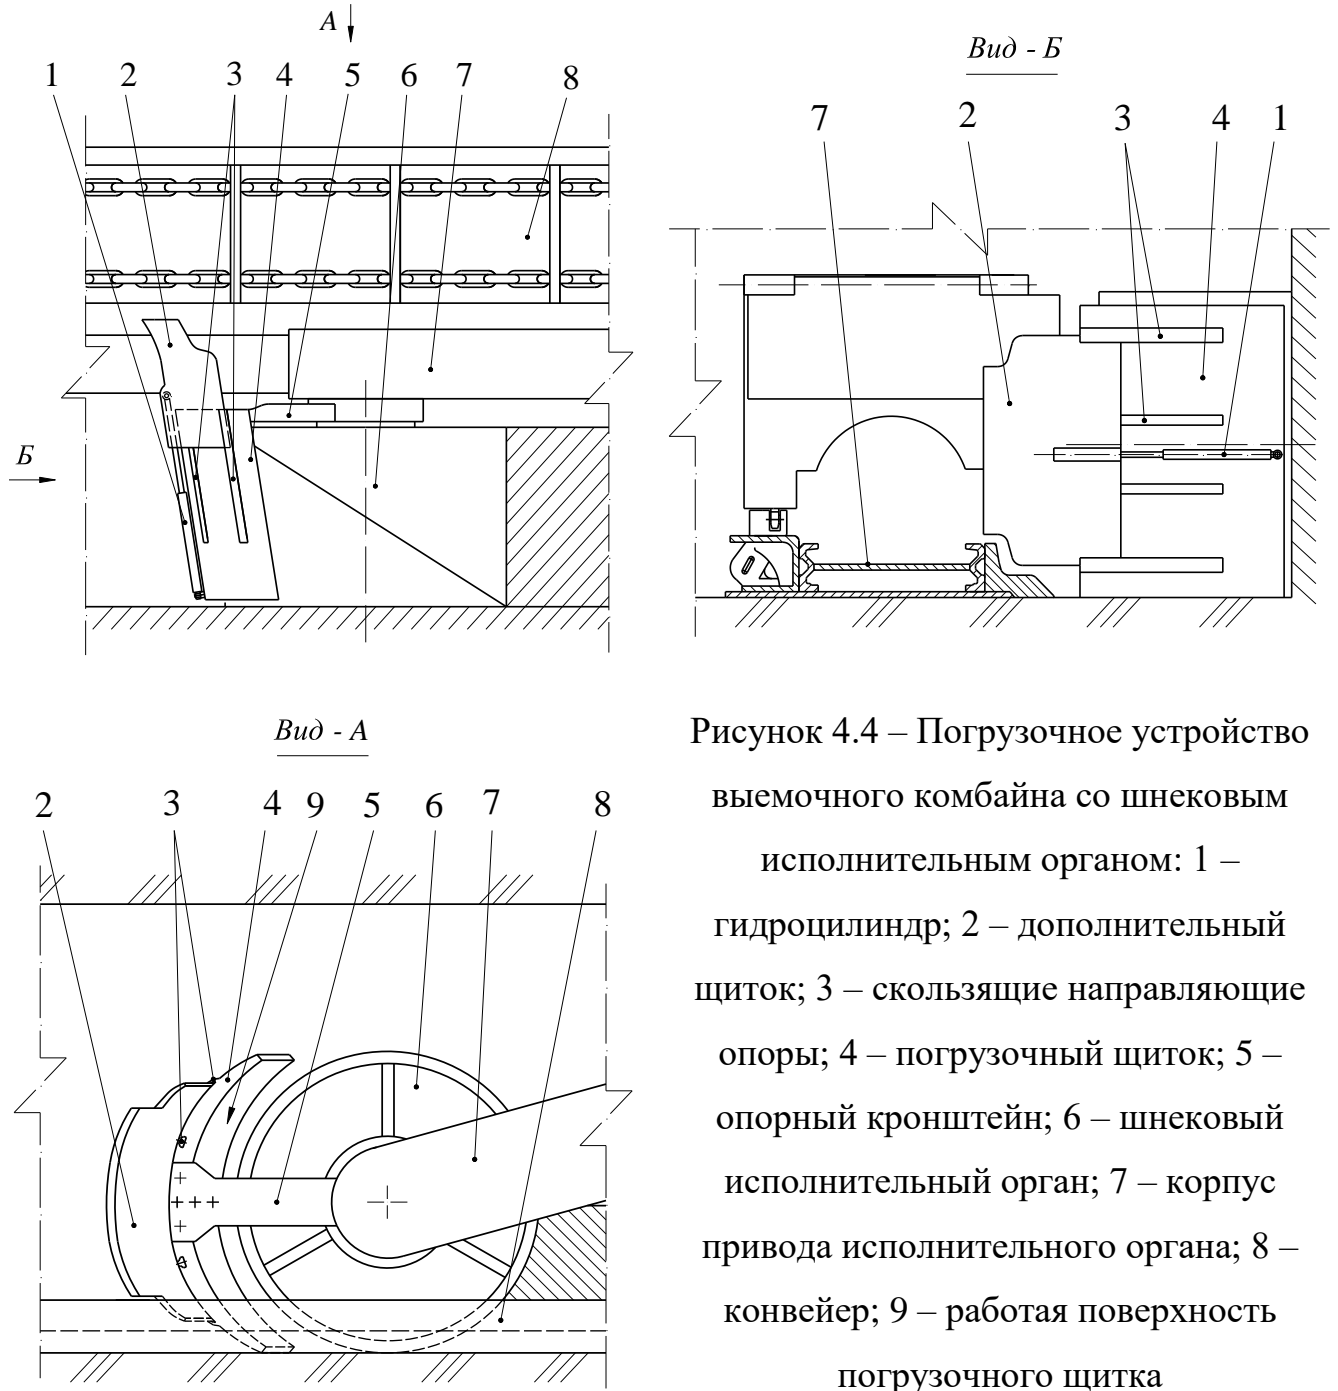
Погрузочное устройство выемочного комбайна со шнековым исполнительным органом: 1 – гидроцилиндр; 2 – дополнительный щиток; 3 – скользящие направляющие опоры; 4 – погрузочный щиток; 5 – опорный кронштейн; 6 – шнековый исполнительный орган; 7 – корпус привода исполнительного органа; 8 – конвейер; 9 – рабочая поверхность погрузочного щитка
